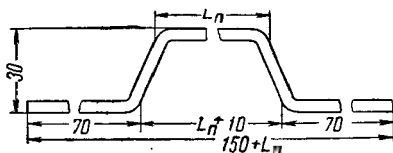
Опорная скоба для намотки «впротяжку» (размеры в мм);  $L_n$  — длина паза.
